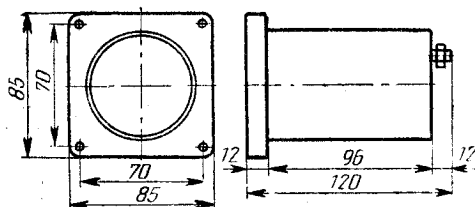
Габаритный чертеж прибора типа Э144.
